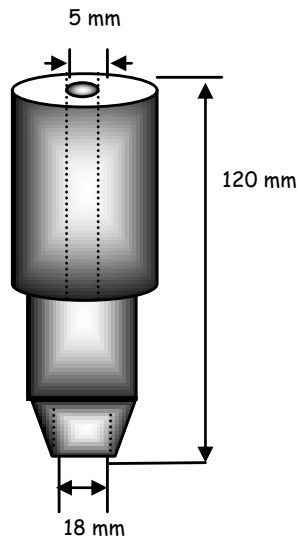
Moule utilisé pour la découpe des pastilles.
